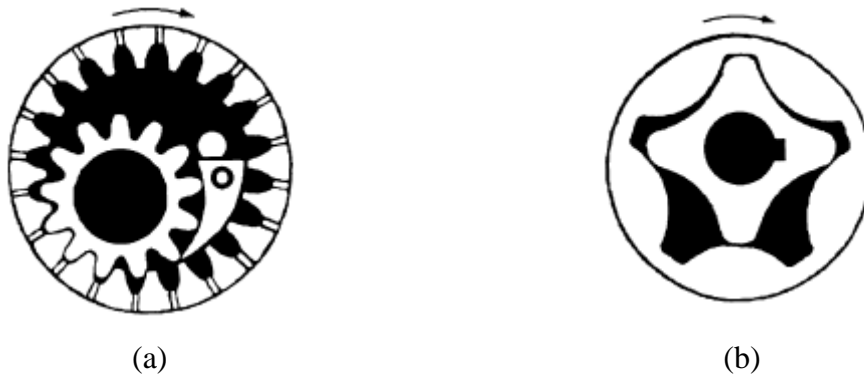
Detalhe dos rotores das bombas de engrenagens internas (a) bomba de engrenagens; (b) bomba de gerotores. Adaptado de LINSINGEN, 2001
